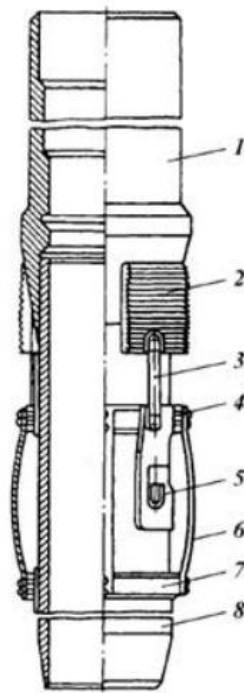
Механическая клиновая подвеска: 1 – конусообразная муфта; 2 – клиновые плашки; 3 – соединительная пластина; 4,7 – верхнее и нижнее кольца центратора; 5 – штифт; 6 – пружинный центратор; 8 – корпус
